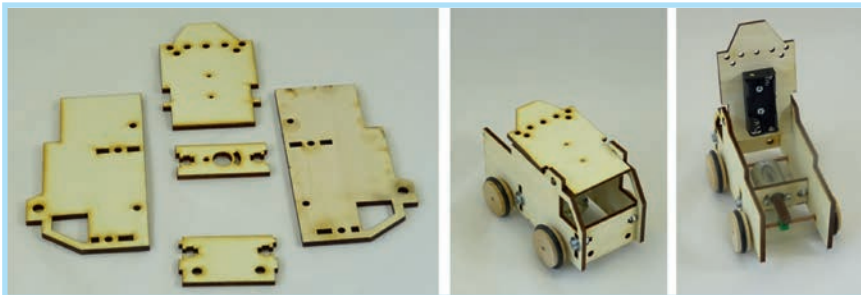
Lasergeschchnittene Bauteile und montiertes Fahrzeug mit Motor & Getriebe sowie Batteriekasten
